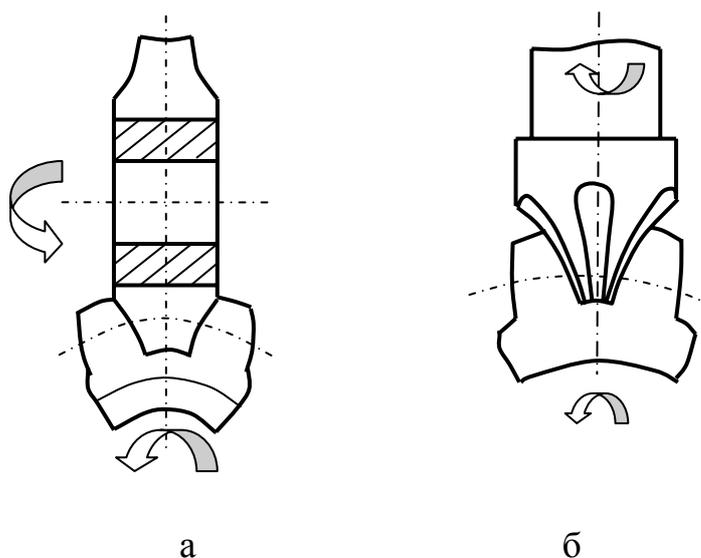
Схема нарезания зубчатых колёс модульными фрезами:
